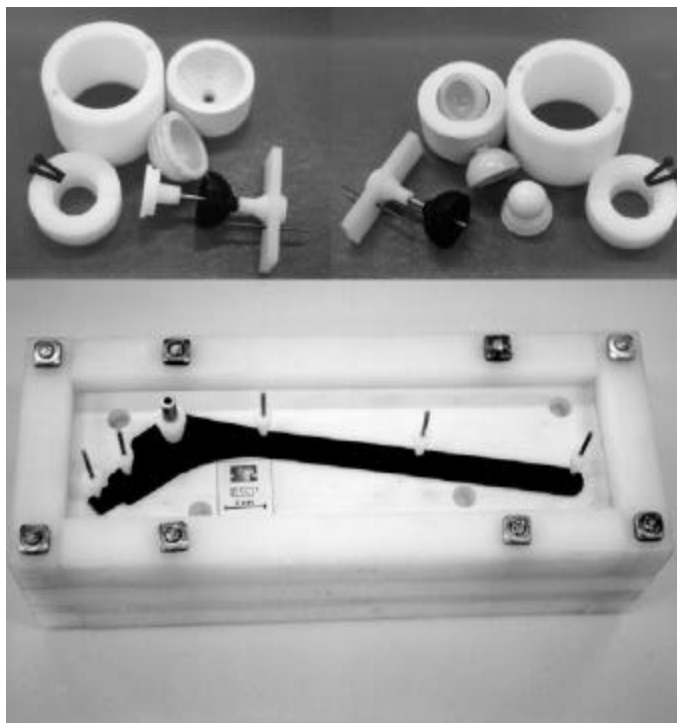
Componentes e moldes do implante de quadril, projetados e construídos utilizando técnicas de CAD/CAE e prototipagem rápida.
